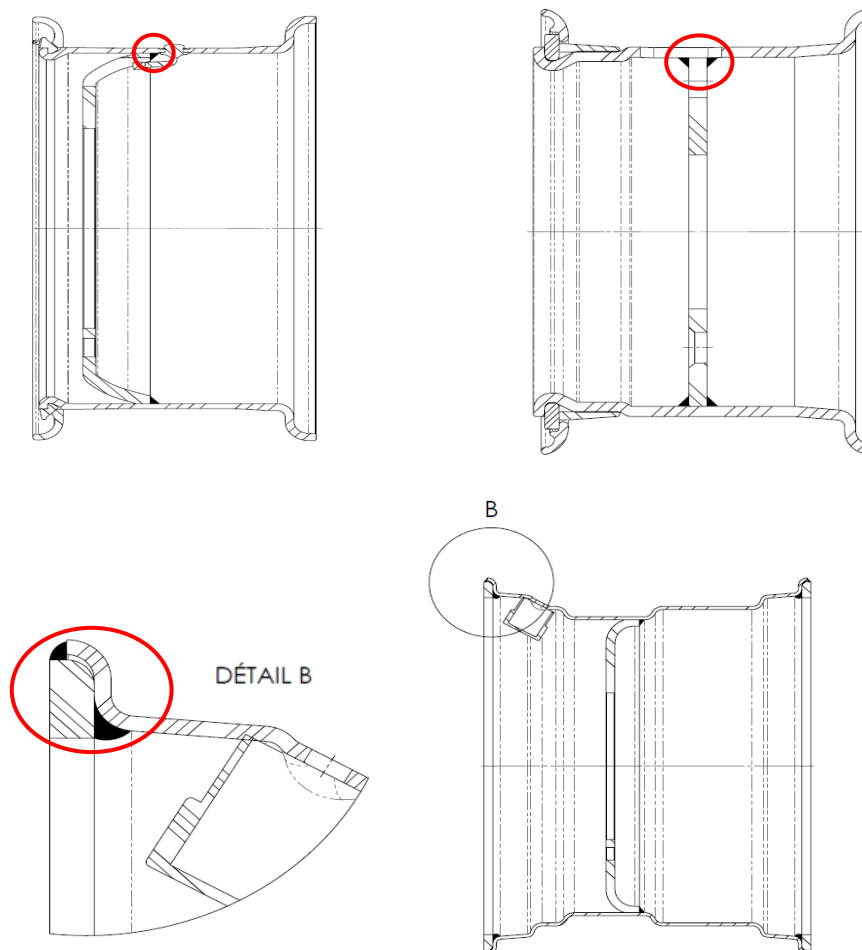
Vue en coupe des soudures à automatiser
